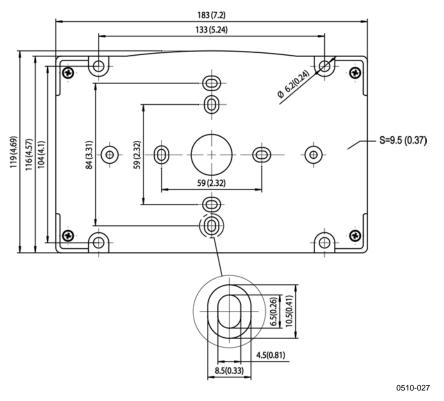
Dimensions de la plaque de montage plastique (mm/pouce)
